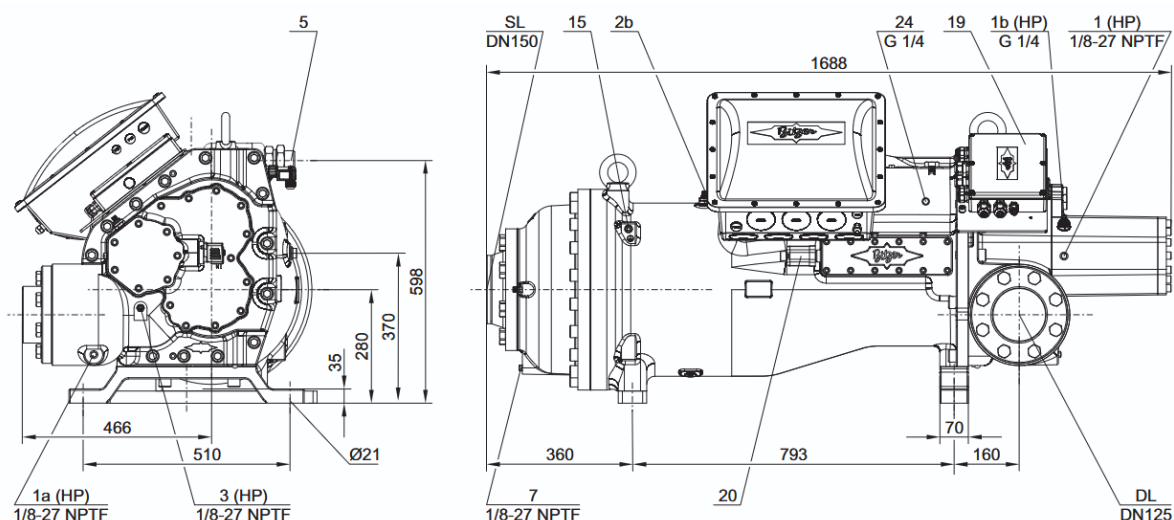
Габаритні розміри компресора HSN95103-280
